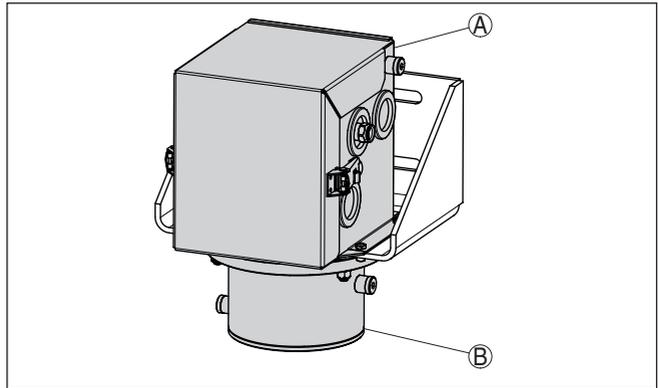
Aktives Luft-Kühlsystem mit Befestigungswinkel
